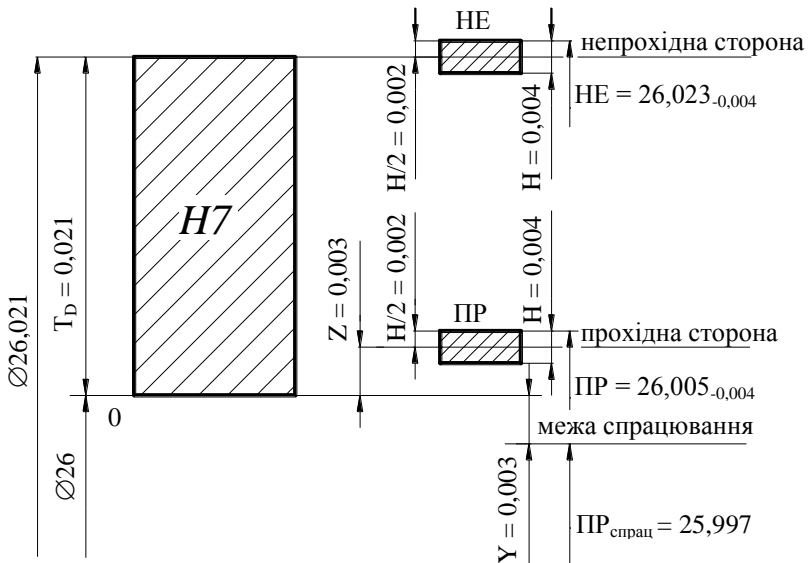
Схема розміщення полів допусків калібр - пробки $\varnothing 26 \text{ H7}$
